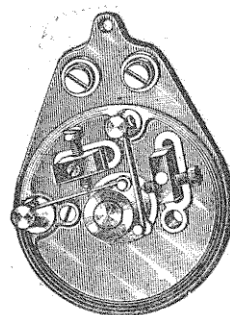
Came d'allumage à bossage pour moteur à deux cylindres
